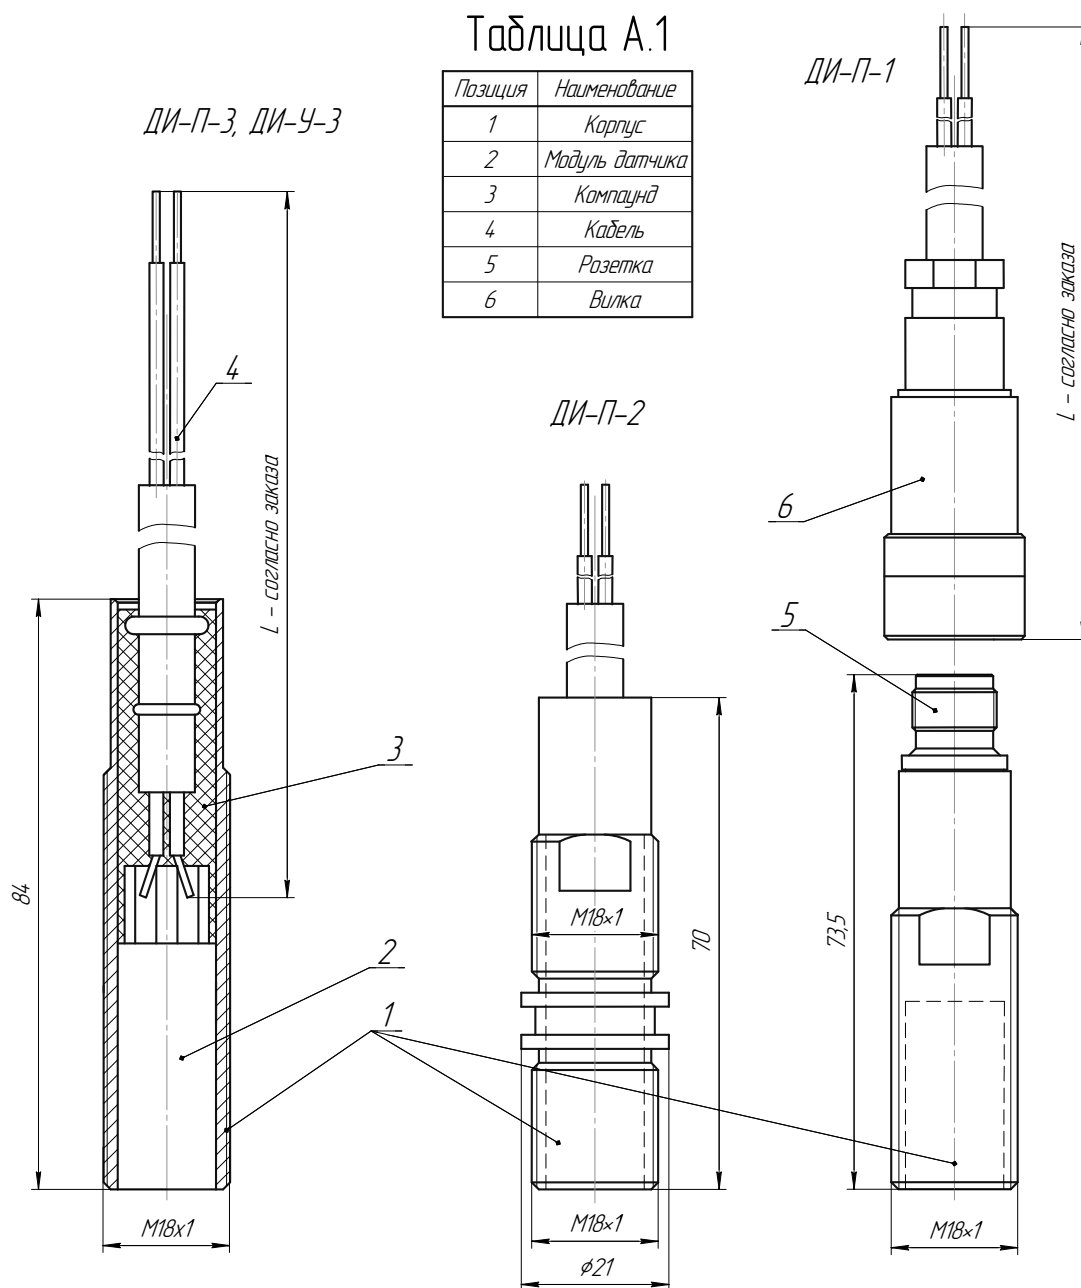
Датчики индукционные. Устройство, габаритные и присоединительные размеры.
